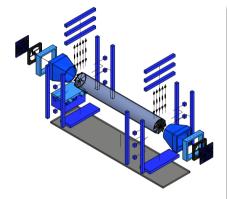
Vista explosionada del modela CAD del dispositivo experimental.
